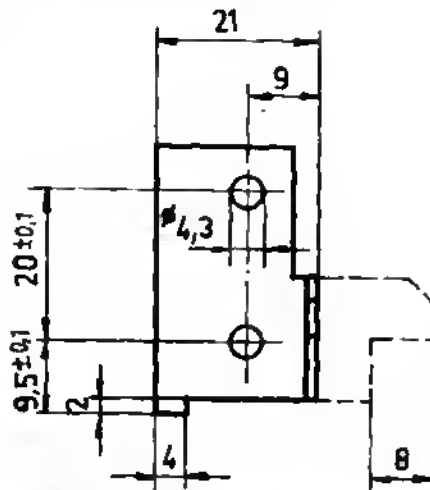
Durchbruch in der Gehäuserückwand bei Bedarf für einen Kabelsteckverbinder
